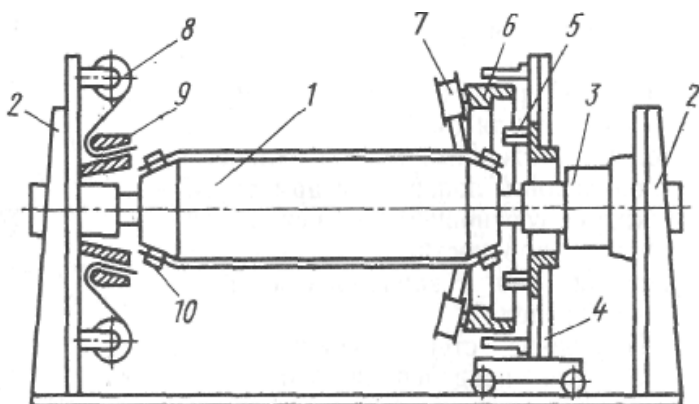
Станок для формования цилиндрических оболочек с продольно-поперечным армированием
